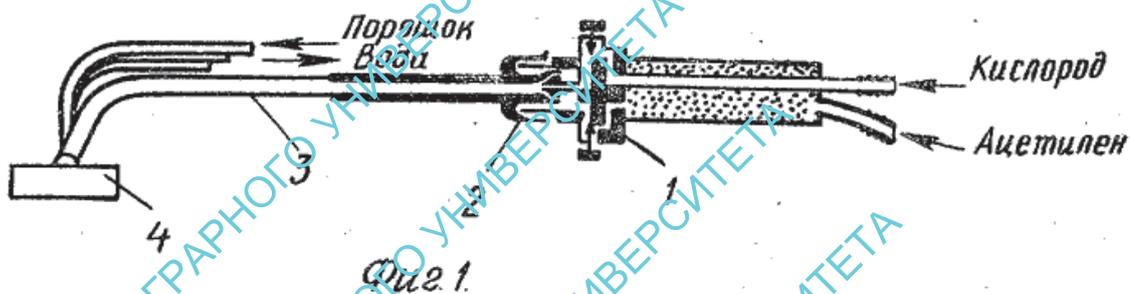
Горелка для газопламенного напыления покрытий из тугоплавких порошков.
